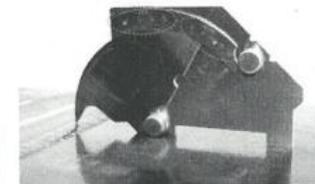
Medición de longitud de soldadura de fillet.
